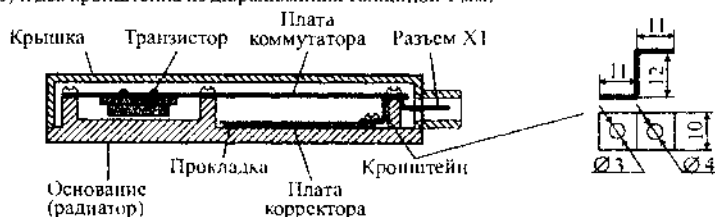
Схема установки платы ОК в корпус коммутатора 3620.3734.
